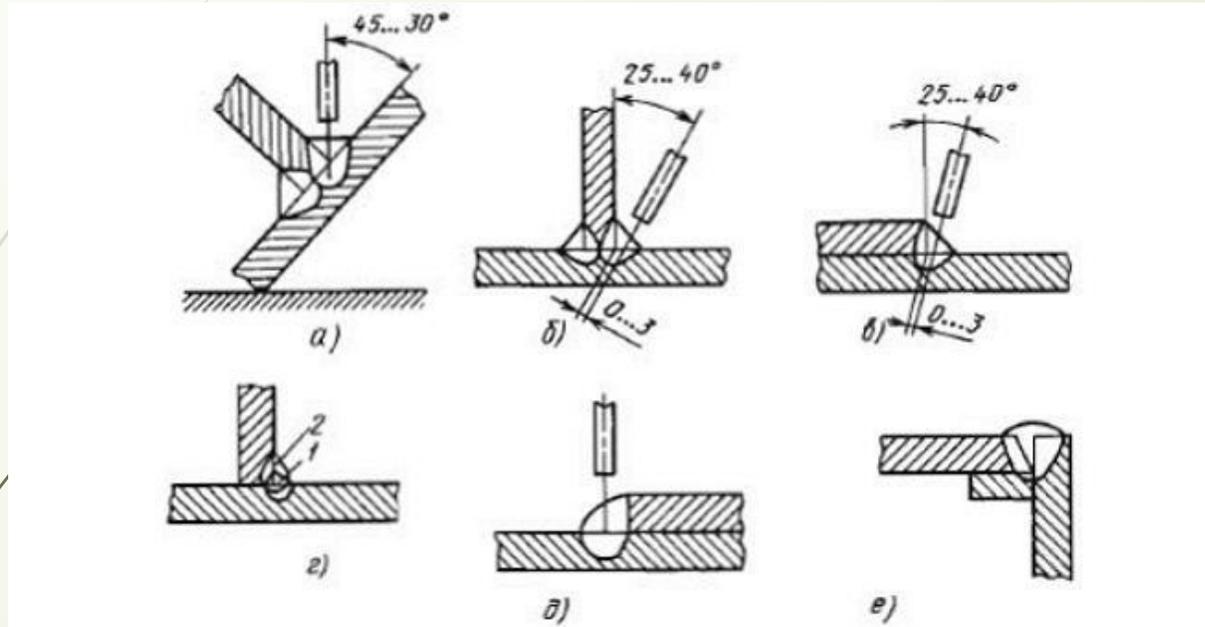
Схемы сварки угловых швов: 1 и 2 - первый и второй проходы.
